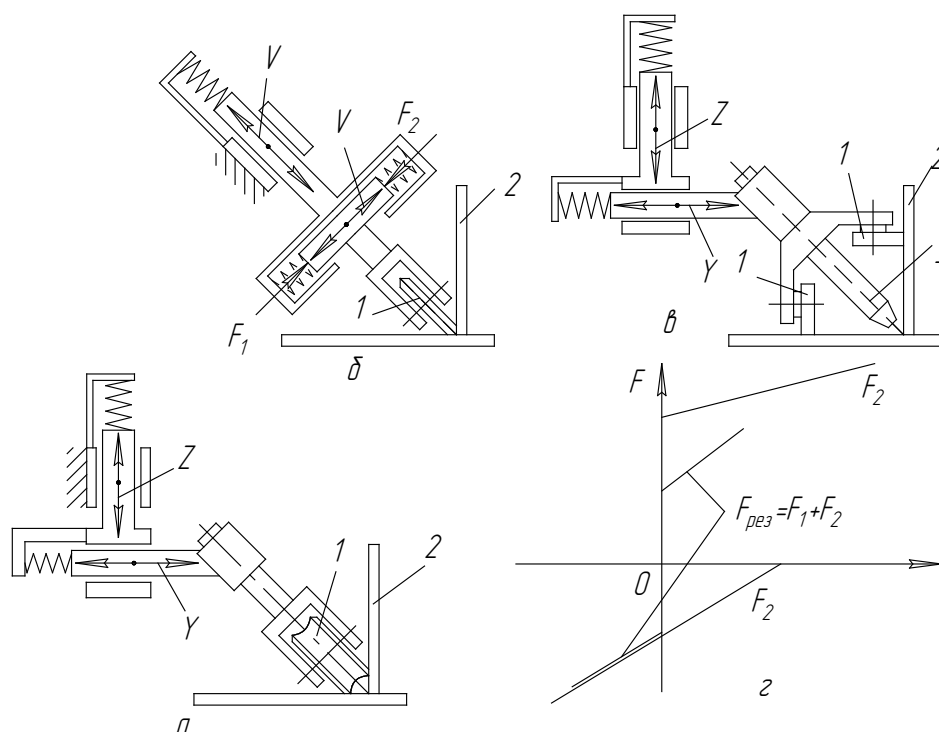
Схеми двокоординатних пристроїв прямої дії для зварювання кутових швів:
